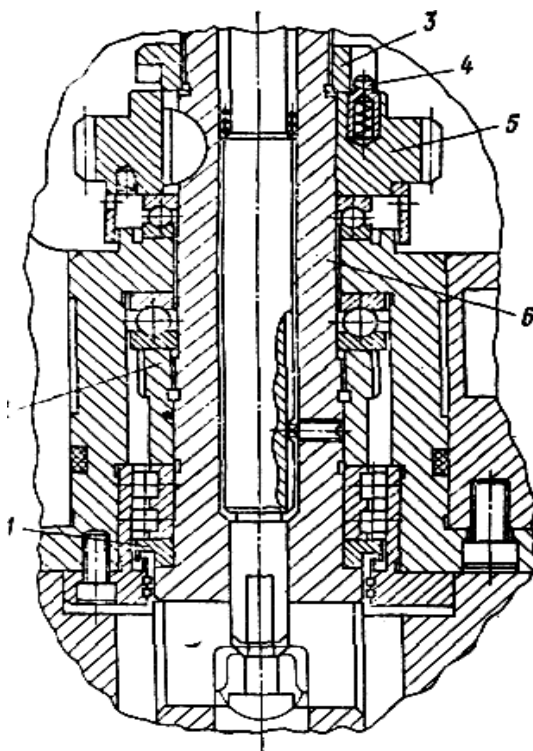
Передня опора шпинделя верстата 2Р135Ф2–1
